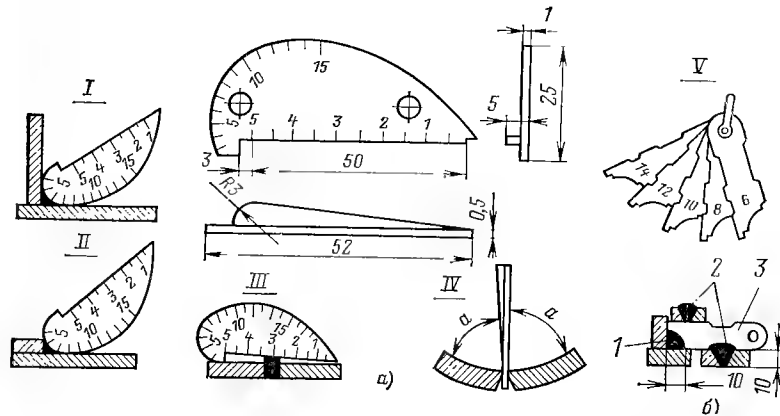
Шаблоны для измерения сварных швов и околошовной зоны. а — универсальный шаблон конструкции А. И. Красовского; б — набор шаблонов; I, II, III — контроль швов таврового, нахлесточного и стыкового соединений; IV — измерение зазора между кромками; I — угловой шов; 2 — стыковые швы; 3 — шаблон.
